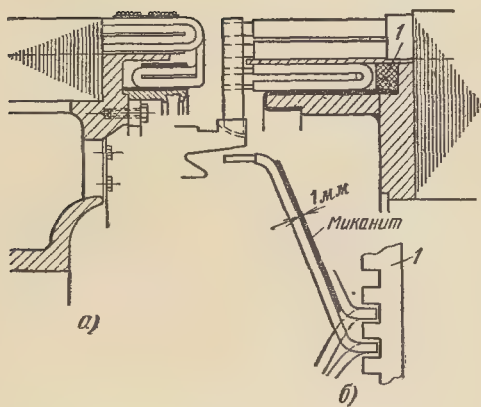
Размещение уравнильных соединений в цилиндрической поверхности.
